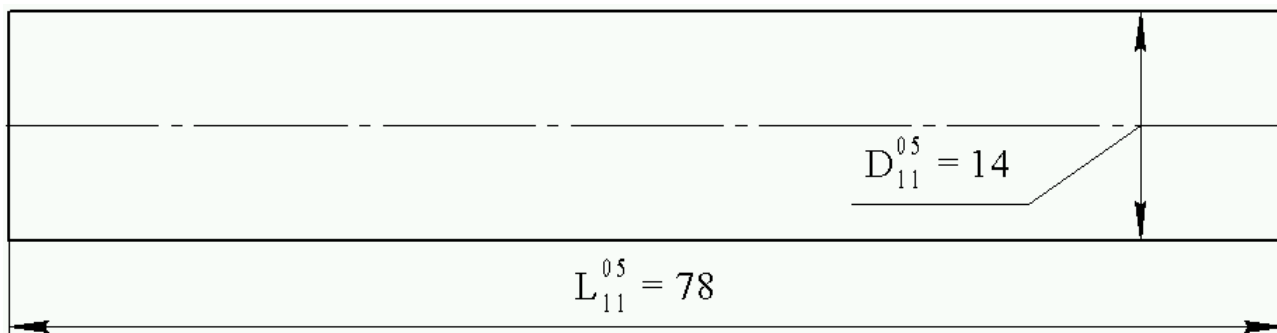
К расчету припусков - Заготовка, Деталь
